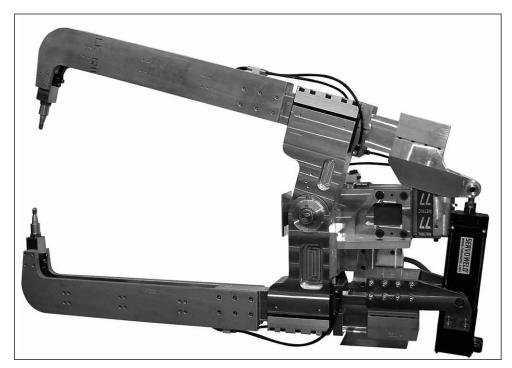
Exemplo de atuador de solda ServoWeld™ (GSWA04) instalado na unidade de pistola de solda estilo "X".
